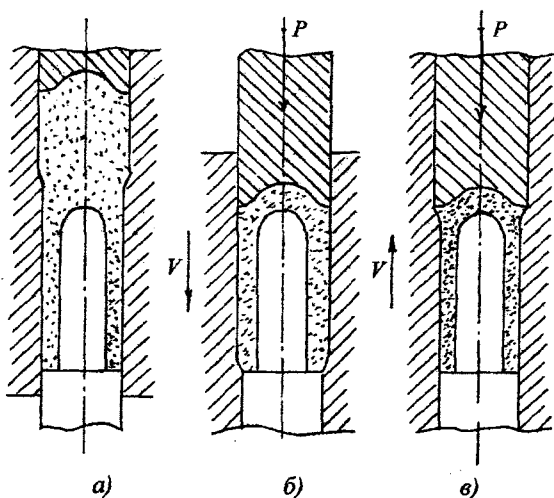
Схема формования стаканов с созданием интенсивных сдвигов в материале порошковой заготовки
